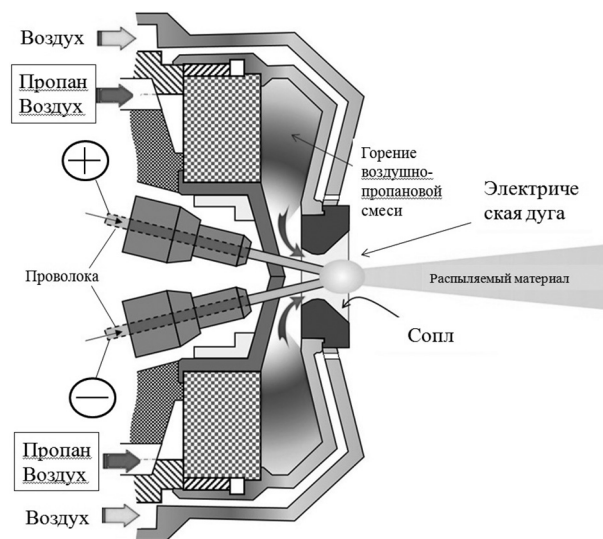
Схема распылительной головки металлизатора установки гиперзвуковой металлизации
